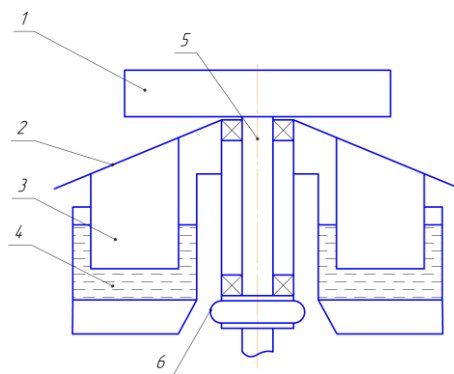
Схема гідростатичного опорного механізму ударно-відцентрової дробарки
